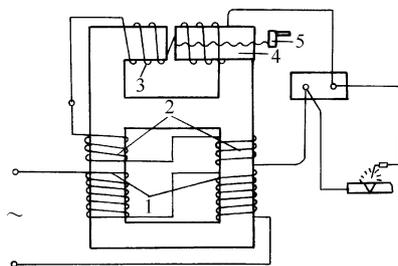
串联电抗器式（同体式）电焊变压器的结构示意图
